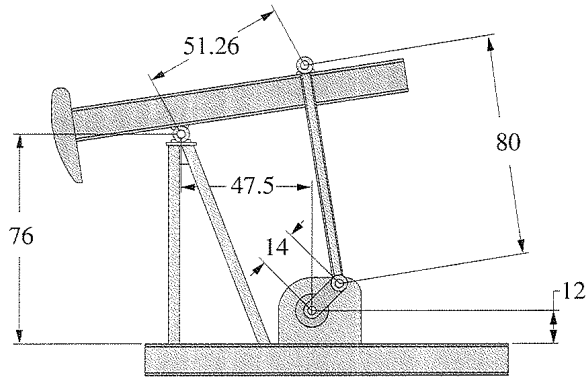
Problema 2-42 Bomba de pozo petrolero; dimensiones en pulgadas
